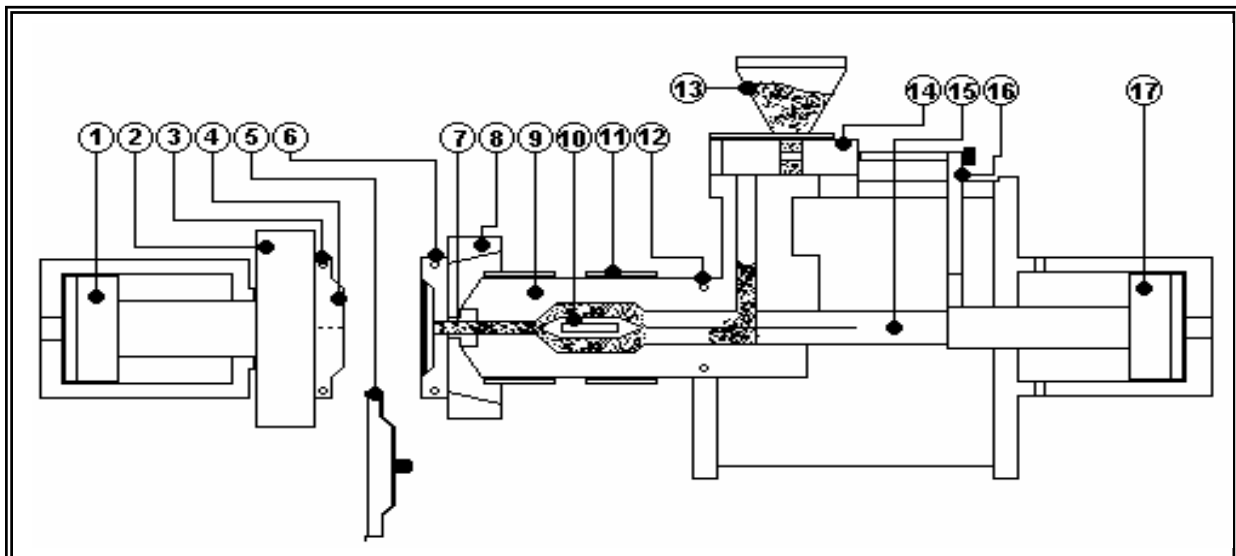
Diagrama simplificado de una maquina de moldeo por inyección tipo pistón. Todos los componentes móviles de la maquina están representados al finalizar el ciclo. Nótese que la pieza moldeada (5) es expulsada del molde-1. Pistón de cierre del molde-2. Platina móvil-3. Circuito de agua para el enfriamiento del molde-4. Medio molde móvil-5. Pieza moldeada-6 Medio molde fijo-7 Boquilla-8 Platina fija-9. Cilindro de plastificación-10 Torpedo-11. Resistencia eléctrica para calentamiento del cilindro de plastificación-12. Circuito de agua para el enfriamiento del cilindro de plastificación-13. Tolva-14. Dosificador-15. Pistón de inyección-16. Brazo que actúa el dosificador-17. Pistón hidráulico de inyección.
